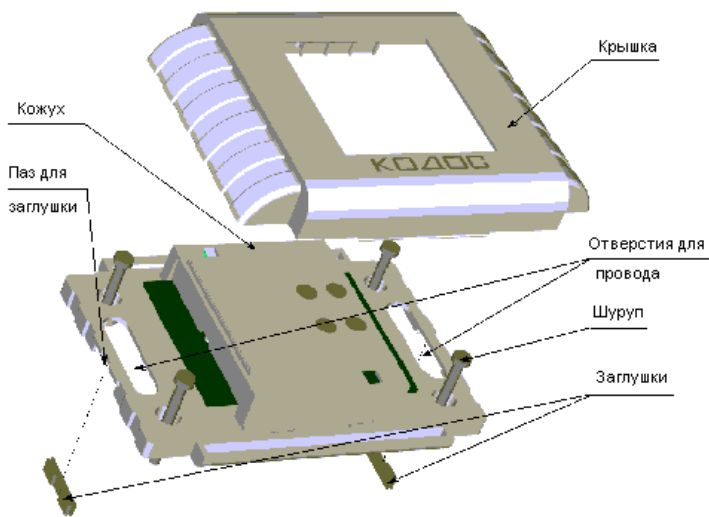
Крепление адресного блока «КОДОС А-09»
